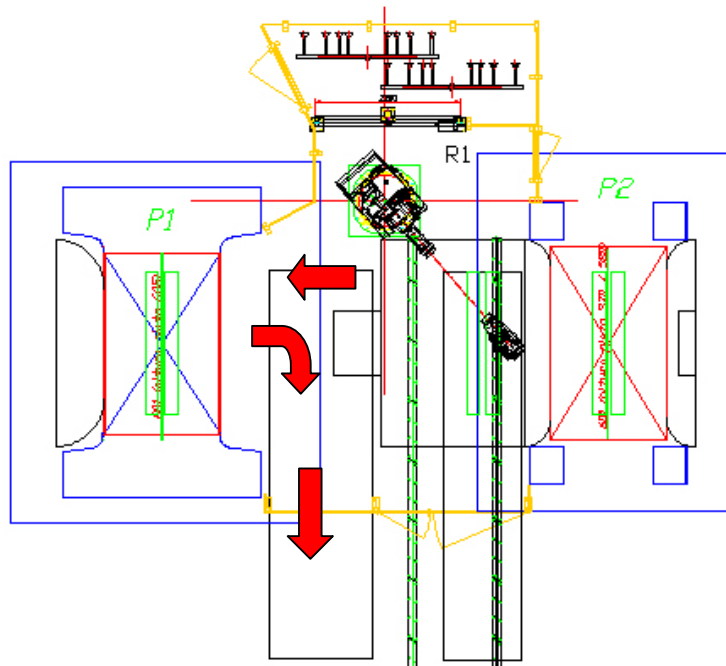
Distribució en planta de la cèl·lula #1 treballant en el mode 1
